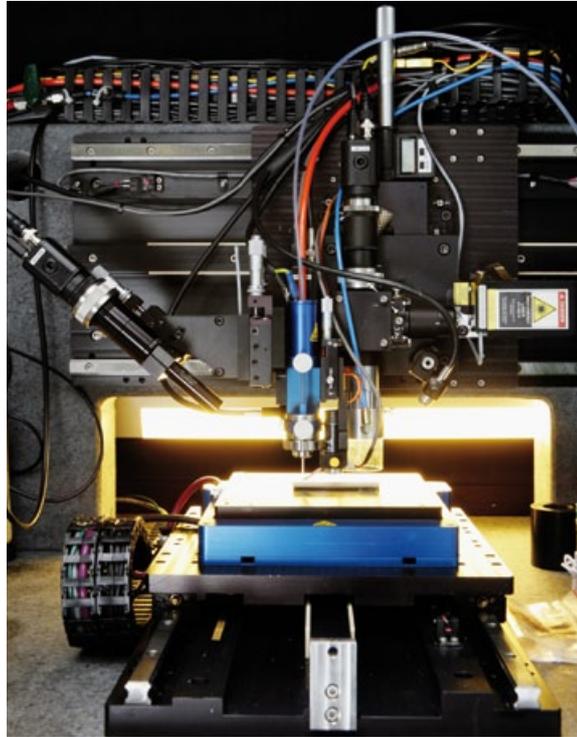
Blick in das Herzstück des Aerosoldruckers für Feinstrukturen.
